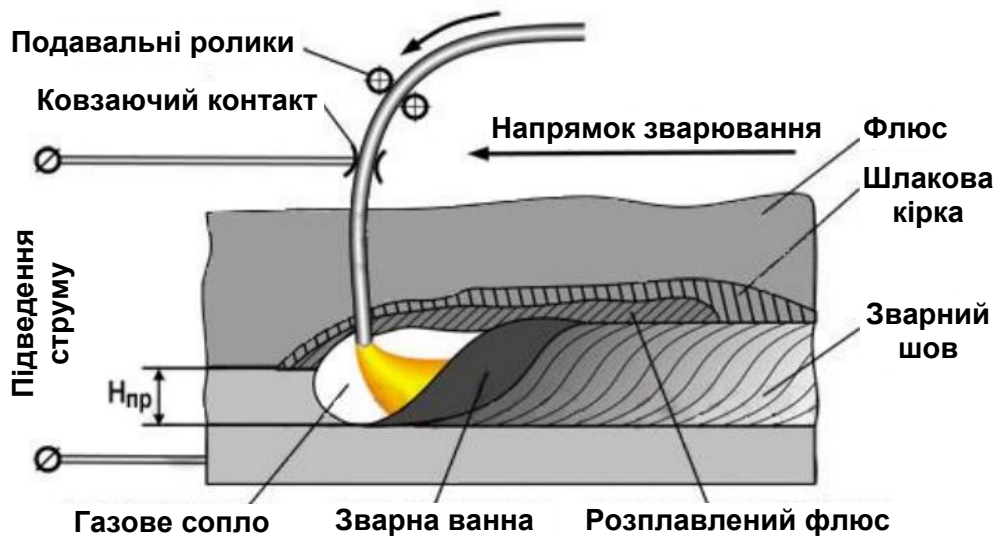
Схема автоматичного зварювання під флюсом
